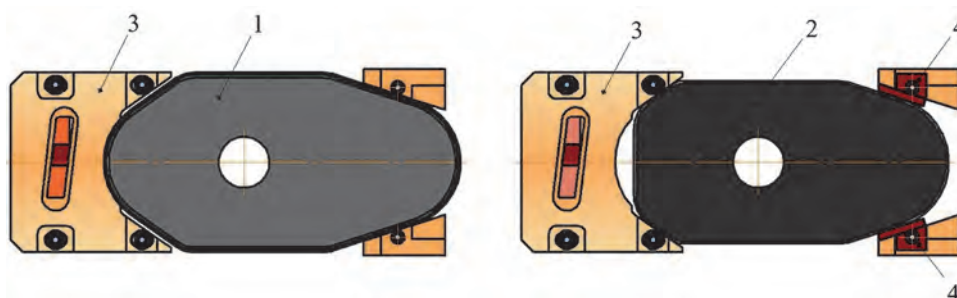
Схема универсального крепления шиберных плит различных типоразмеров в шиберном затворе
